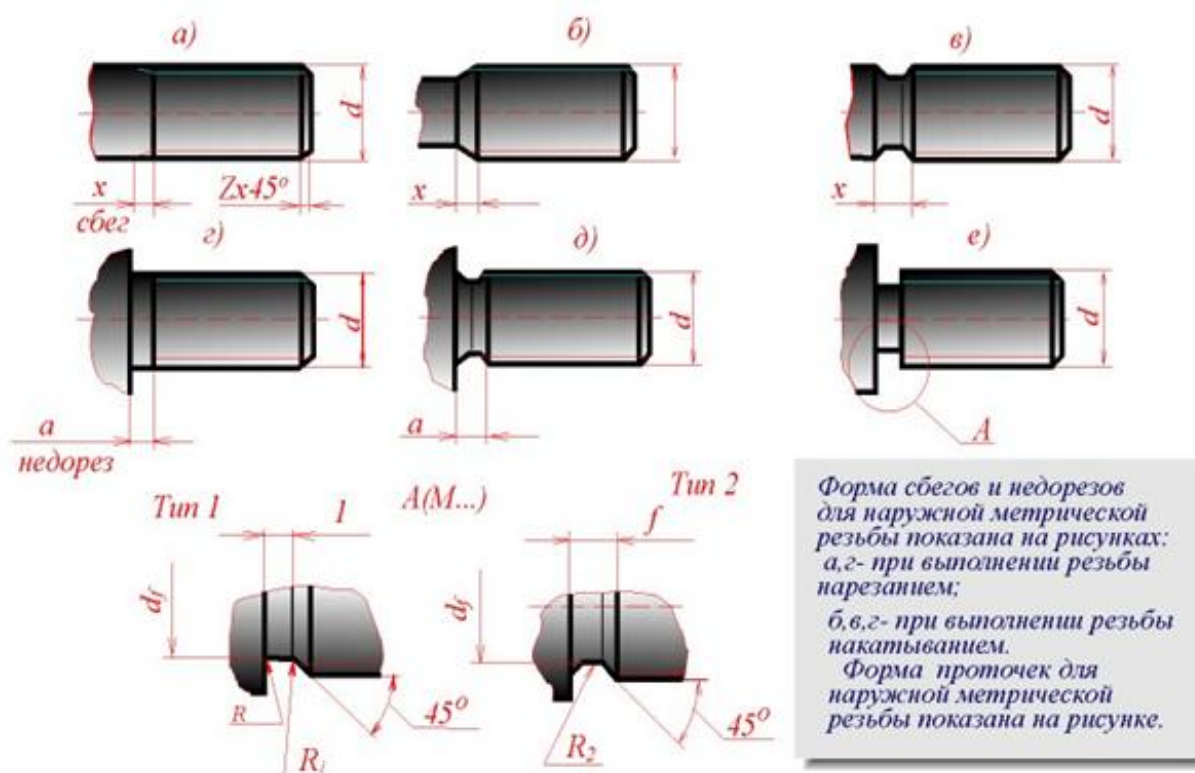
Форма сбегов и недорезов для наружной метрической резьбы
